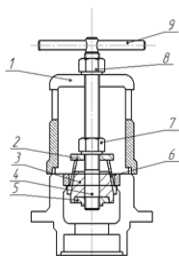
Съемник для выпрессовки обойм с помощью конуса и втулки
